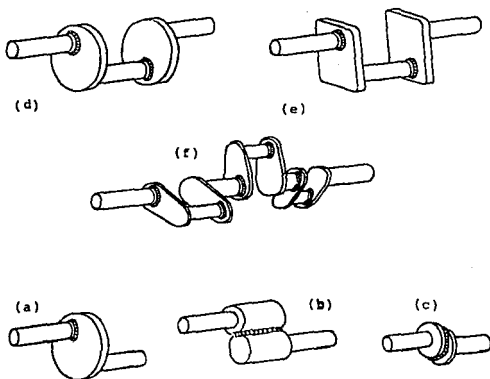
Manivelas y cigueñales soldados.
